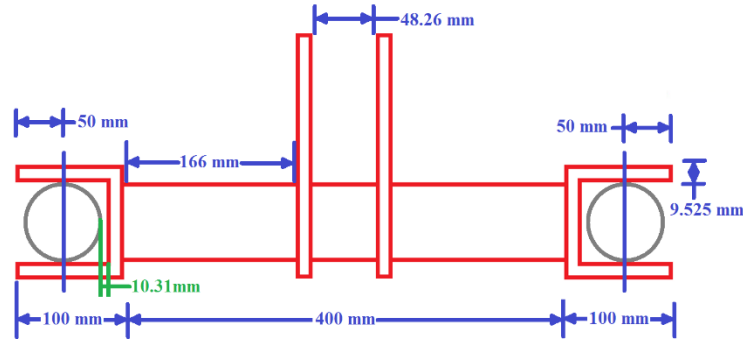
Dimensiones tentativas de la junta, vista lateral
